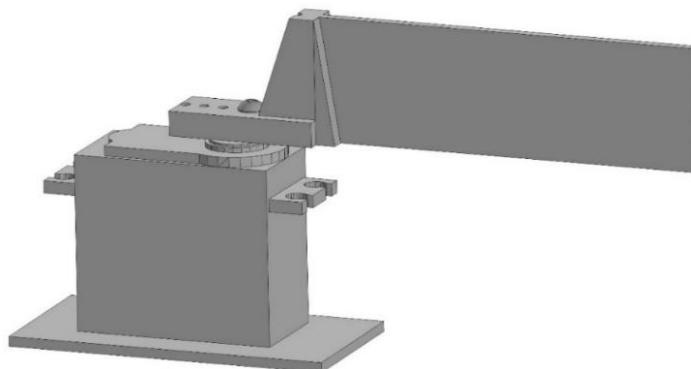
Внешний вид 3D-модели крепления пластины на вал сервопривода TowerPro MG996
